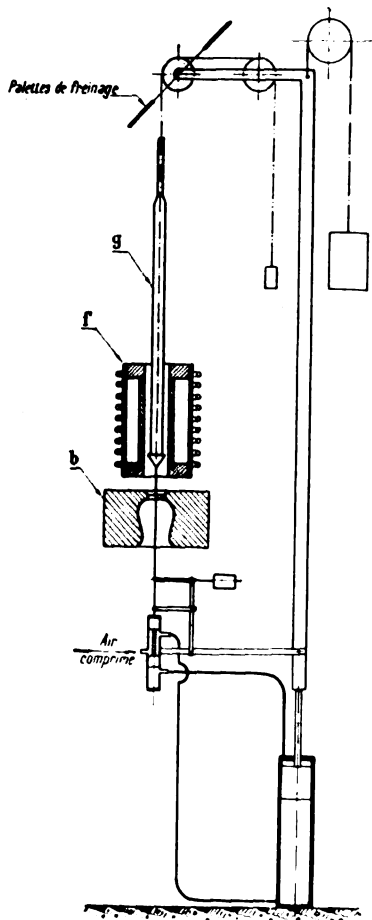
Schéma de la machine automatique à souffler et à mouler.
